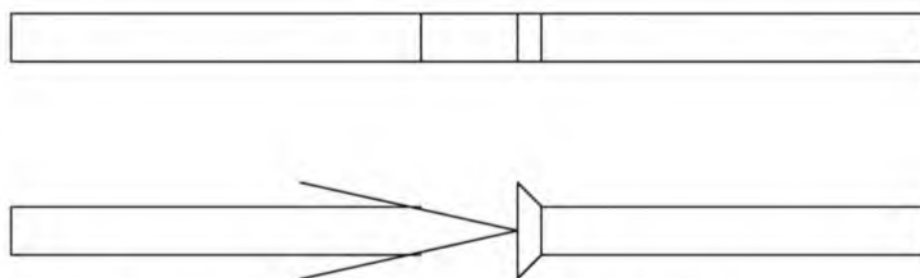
Подготовка торцов под сварку
